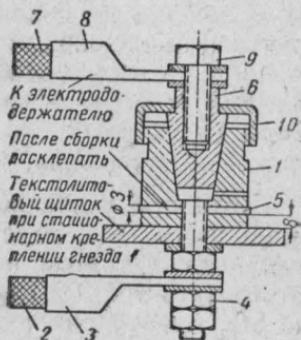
Штепсельное соединение сварочных проводов:
